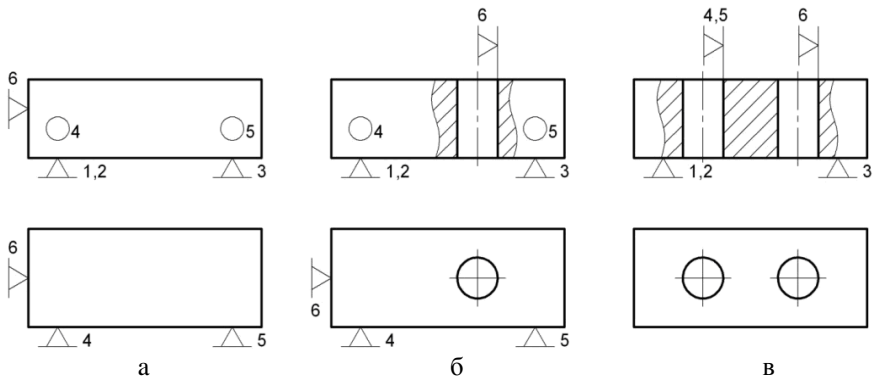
Схеми базування корпусних деталей у ВП
